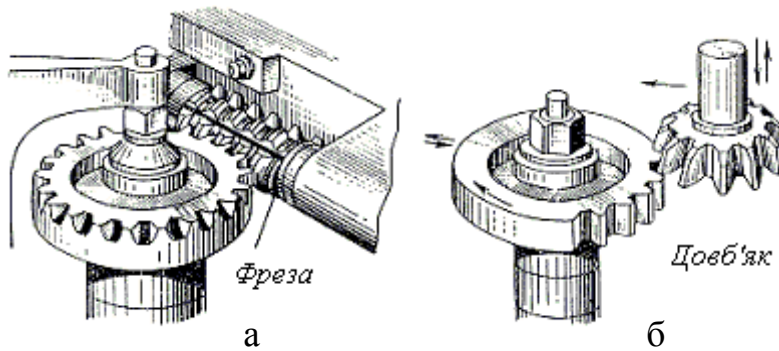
Робоча ділянка нарізання зубчатих коліс: а – черв'ячною фрезою; б – довб'яком.
